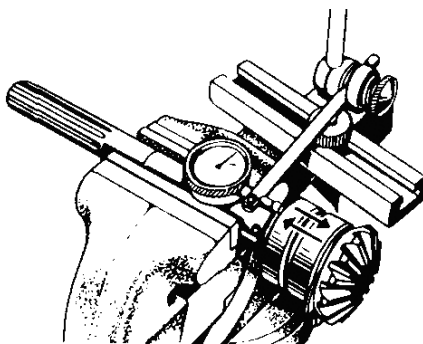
Проверка правильности регулировки осевого зазора в подшипниках полуоси или вертикального вала.
